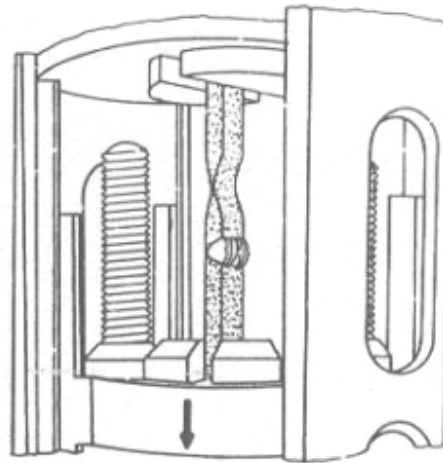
Probeta estándar para pruebas de tensión, para probar soldaduras hechas en placas. (Ilustración redibujada con autorización de la James F. Lincoln Arc Welding Foundation, *Metals and How to Weld Them*, 2a. ed., 1954, 1962, p. 17.)
